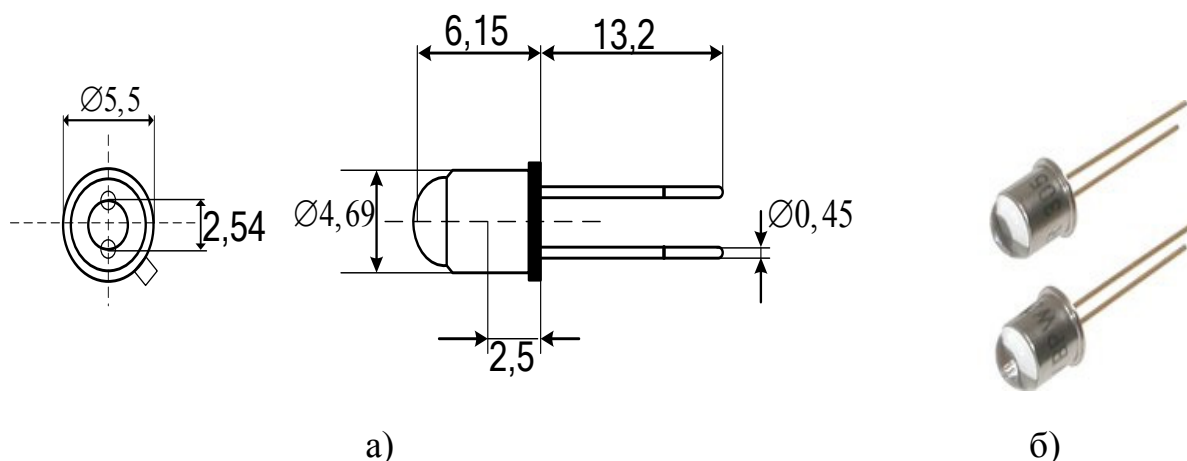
Габарити (а), зовнішній вигляд (б) фотодіода BPW24R
